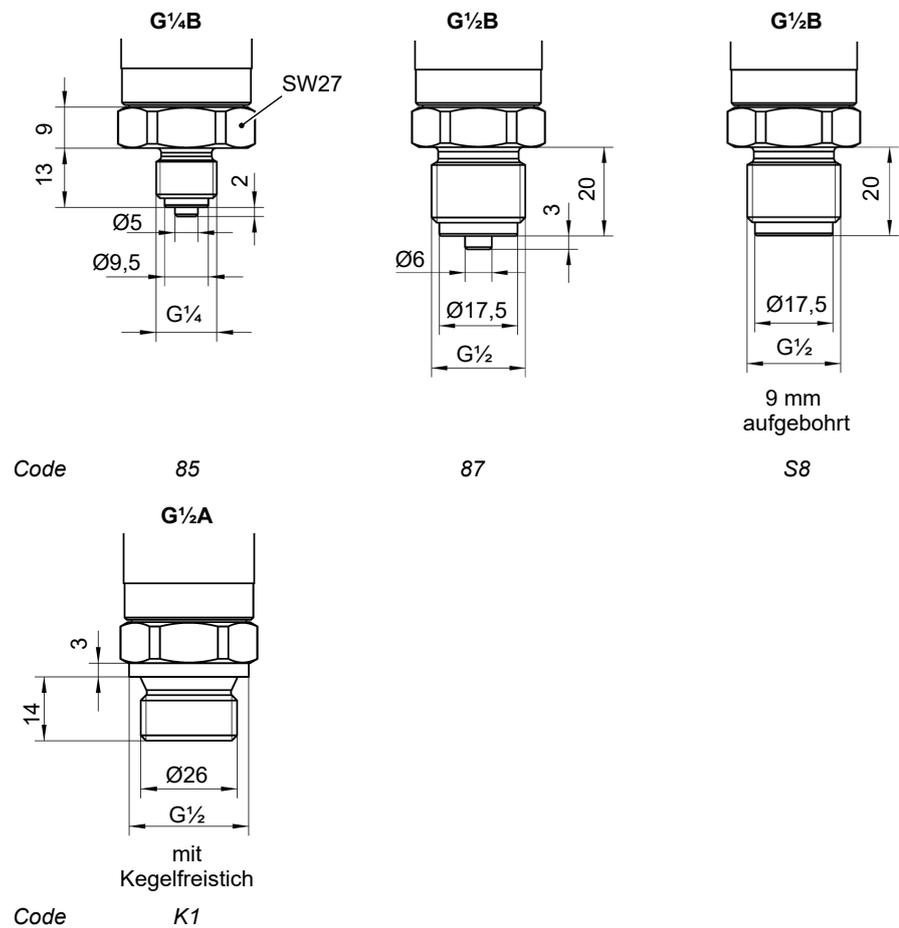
Prozessanschlüsse mit zölligem Gewinde
